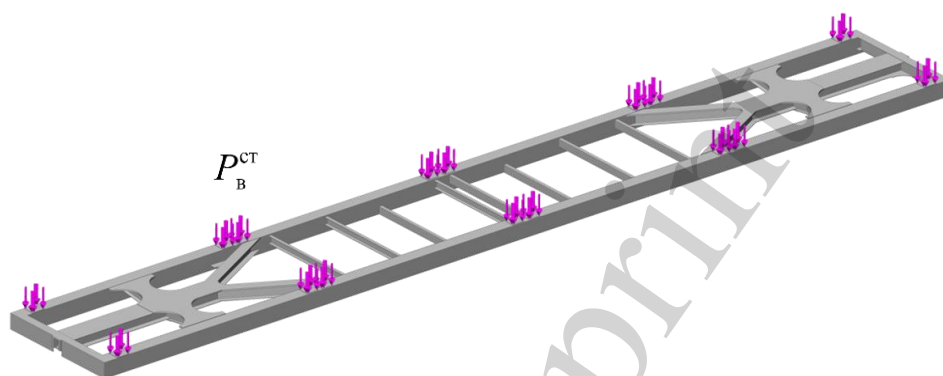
Розрахункова схема несучої конструкції вагона-платформи
